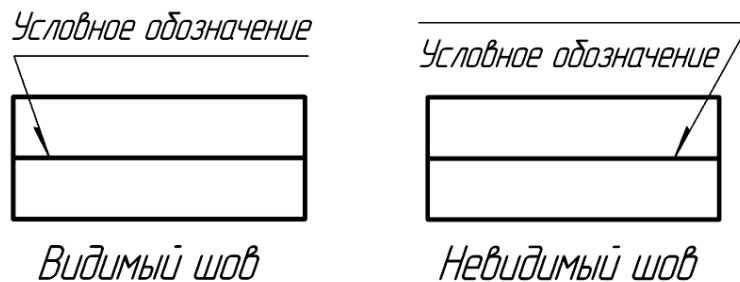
Размещение условного обозначения шва с лицевой и обратной стороны
